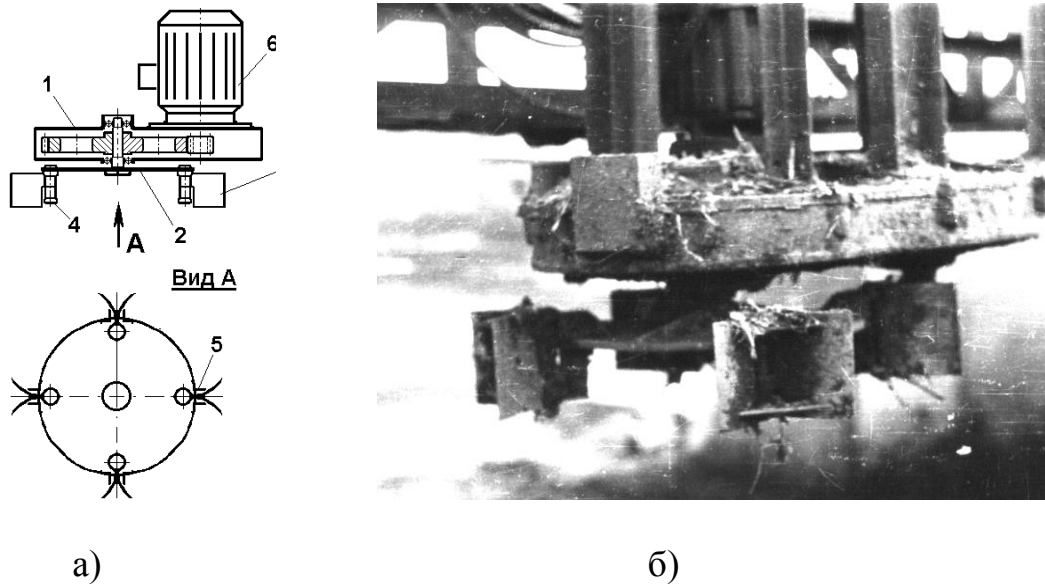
Принципова схема (а) і загальний вид (б) плоскорізального відокремлююче-подрібнювального робочого органу: 1 - корпус; 2 - диск; 3 - лопать; 4 - вісь; 5 - упор; 6 - електродвигун
